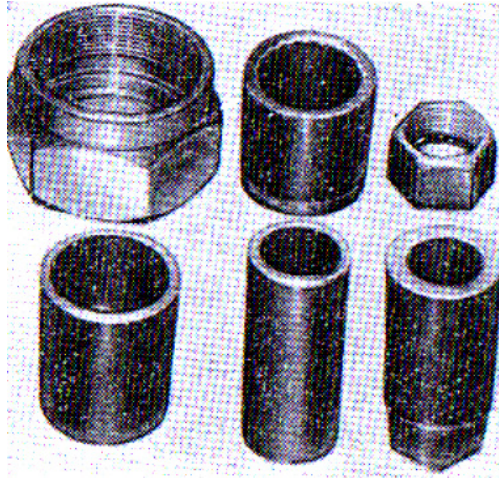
Деталі, заготовки яких отримані зворотним способом видавлювання
